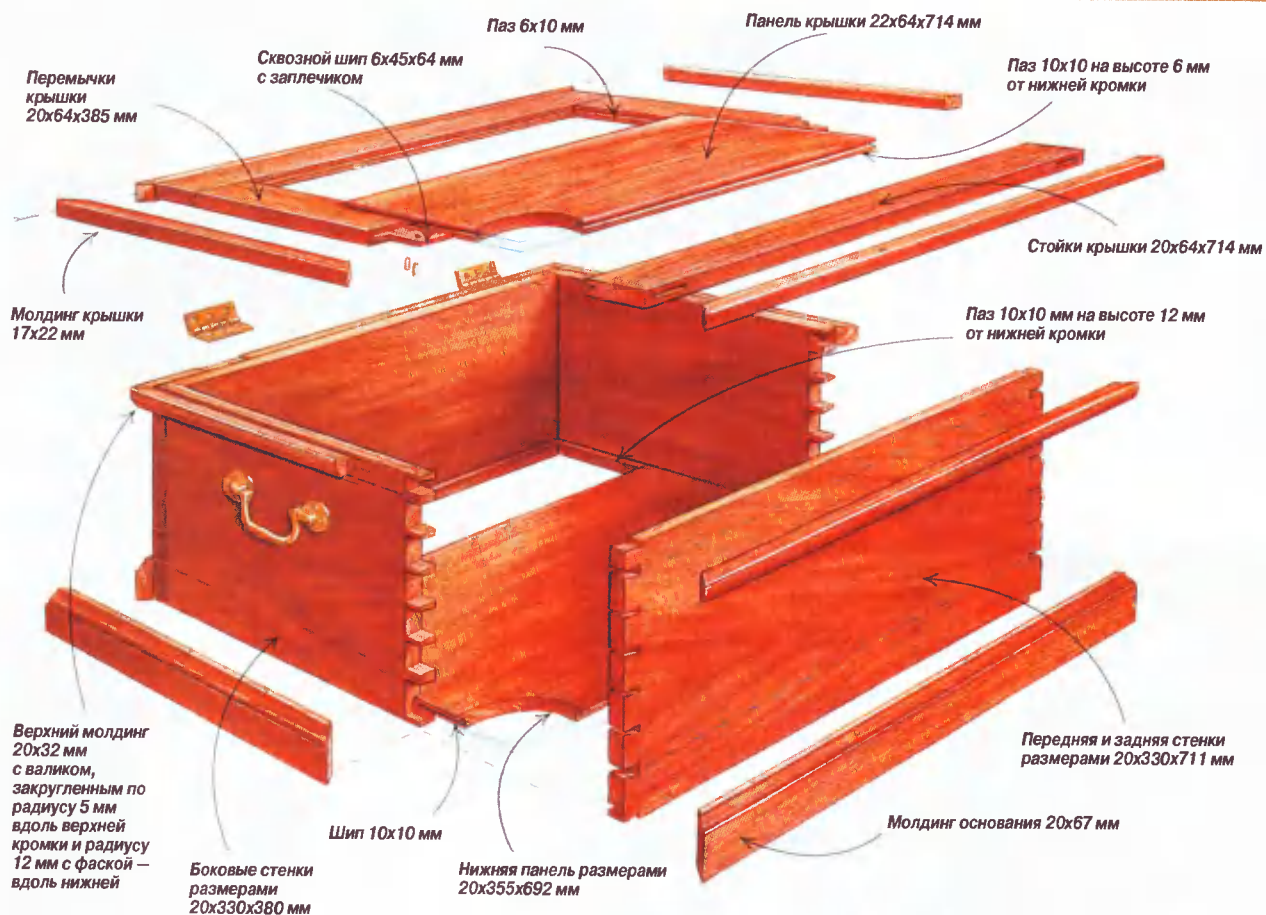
Сундучок для инструментов. Его делают из древесины вишни только ручными инструментами с использованием соединений «ласточкин хвост».
